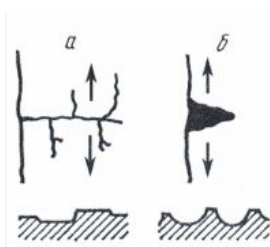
Вид трещины и схема разрушения (сечение перпендикулярно поверхности излома): *a* – хрупкое; *б* – вязкое
